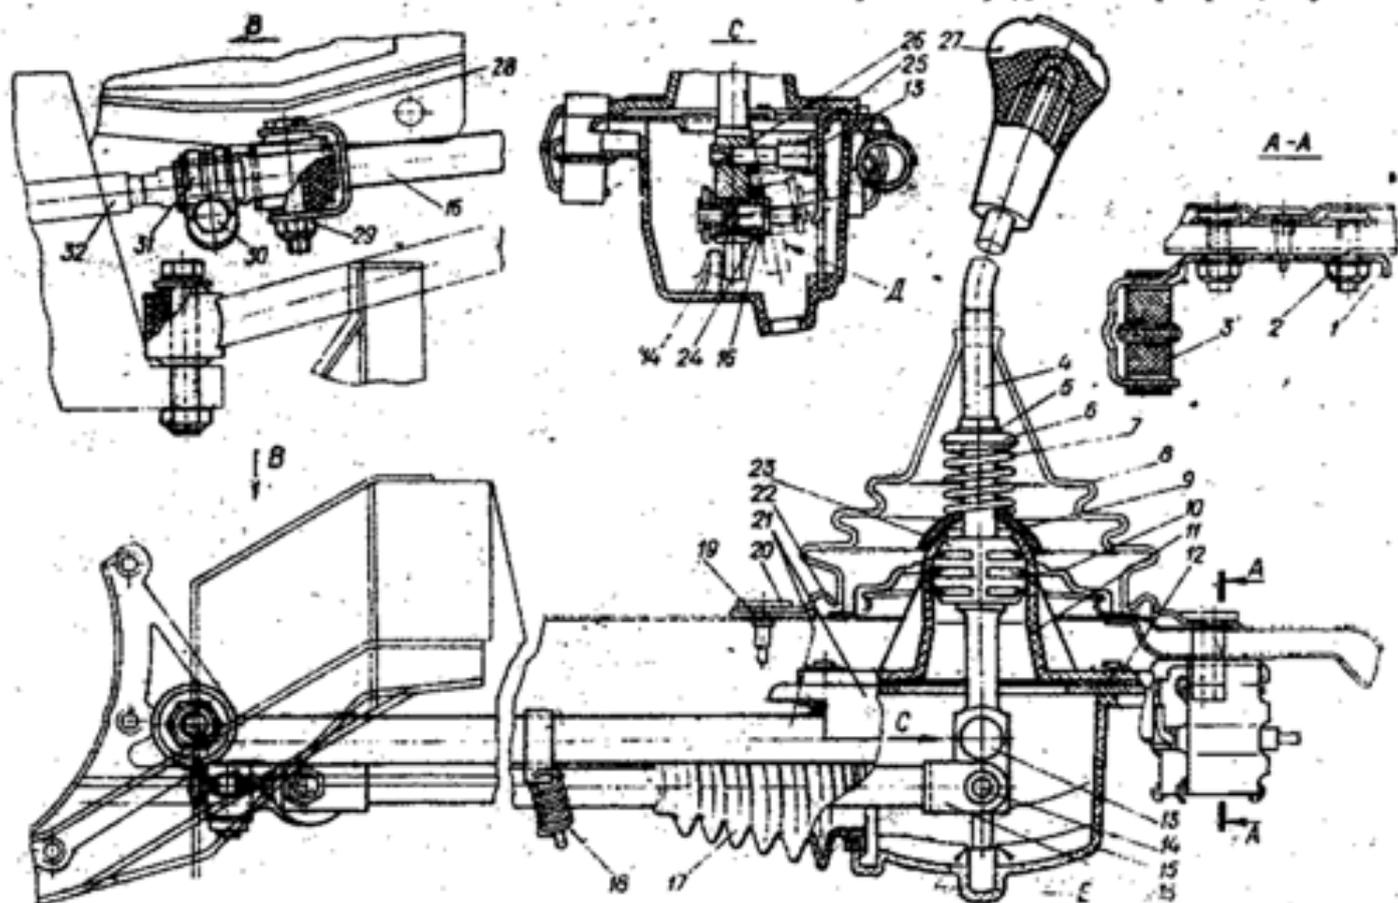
Привод управления механизмом переключения передач: 1 - кронштейн наружный; 2 - гайка М8; 3 - муфта крепления основания; 4 - рычаг переключения передач; 5 - кольцо стопорное; 6 - шайба стопорная; 7 - пружина; 8 - чехол декоративный привода; 9 - чашка упорная; 10 - уплотнитель привода; 11 - опора шаровая; 12 - втулка опоры; 13 - упор подвижный; 14 - упор направляющий; 15 - крышка привода; 16 - вал управления; 17 - чехол защитный; 18 - пружина возвратная; 19 - втулка пистона; 20 - пистон; 21 - основание привода; 22 - крышка чехла; 23 - шарик рычага; 24 - втулка опорная; 25 - кронштейн упора; 26 - пружина подвижного упора; 27 - рукоятка рычага; 28 - болт стяжной; 29 - гайка М10; 30 - болт крепления хомута; 31 - хомут стяжной; 32 - хвостовик вала коробки передач; 33 - втулка амортизационная; 34 - болт реактивной штайги; 35 - втулка внутренняя; Д - положение рычага при установке и регулировке привода управления механизмом переключения передач, соответствующее выбору пятой передачи - заднего хода; Е - нейтральное положение рычага.
